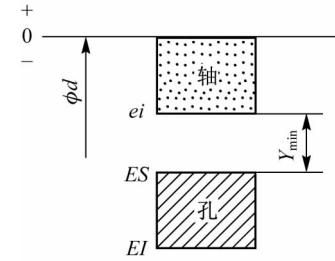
基轴制过盈配合的孔、轴公差带图
